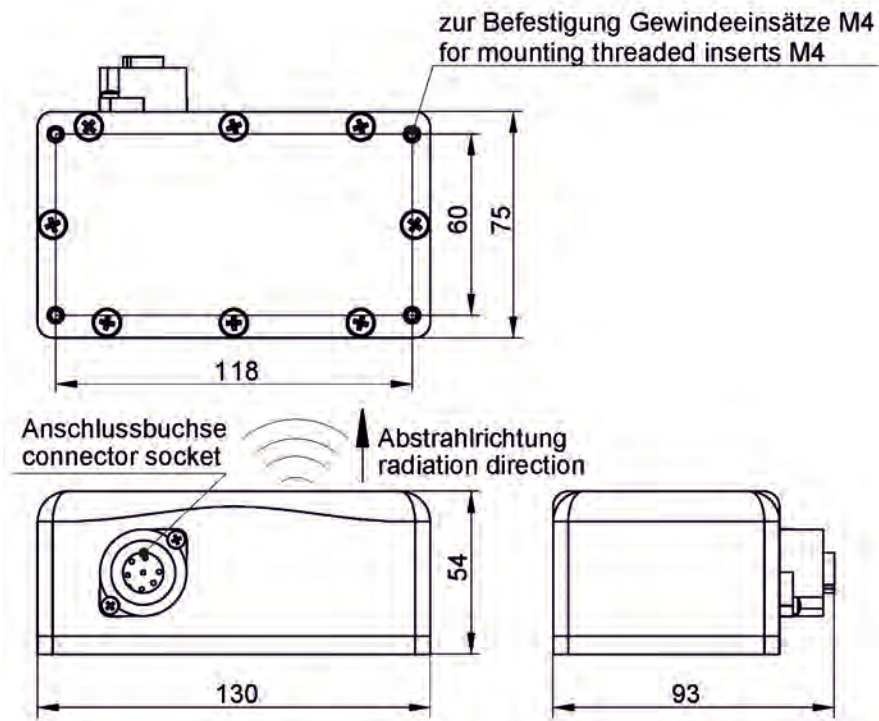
Dimensions du capteur radar OFR types G00/EV0 dans le boîtier du capteur
